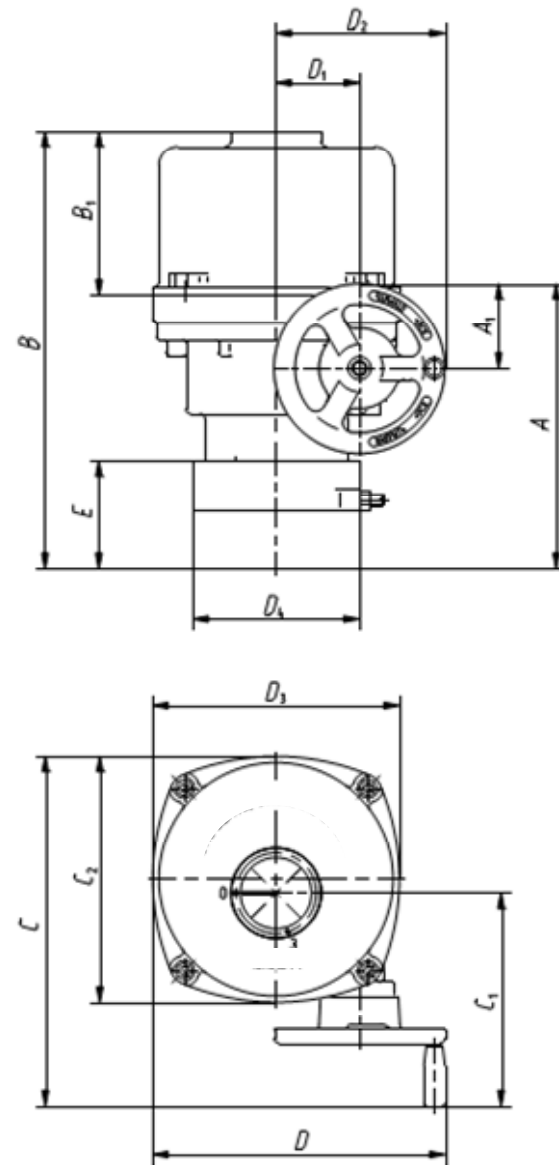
г – Габаритные размеры привода конструктивных схем 12 и 32
